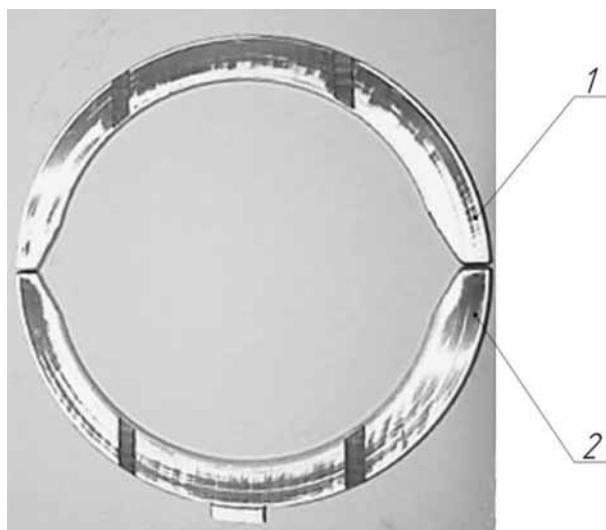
Внешний вид верхнего (1) и нижнего (2) полуколец переднего осевого подшипника коленчатого вала после стендовых испытаний двигателя
